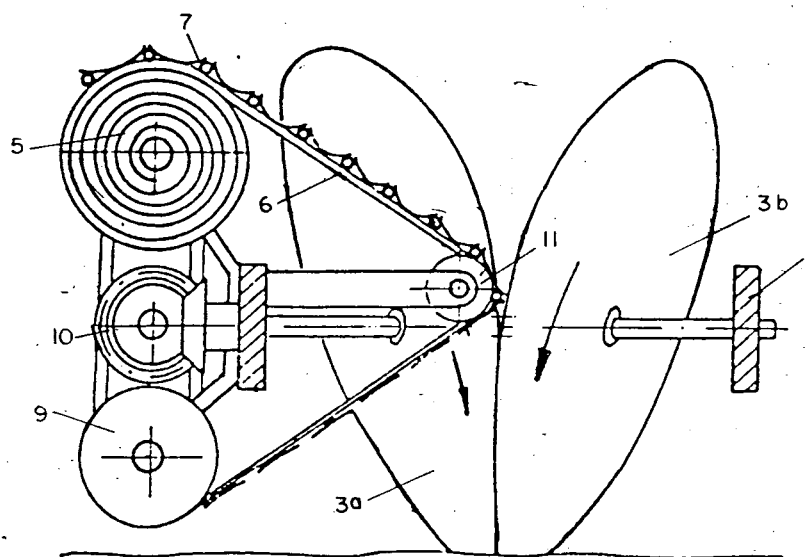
Detalhe do conjunto plantador |7|.
